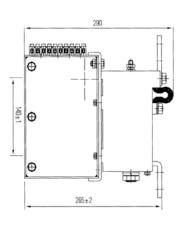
Габаритные размеры КВТ-1,14-1000/1250
